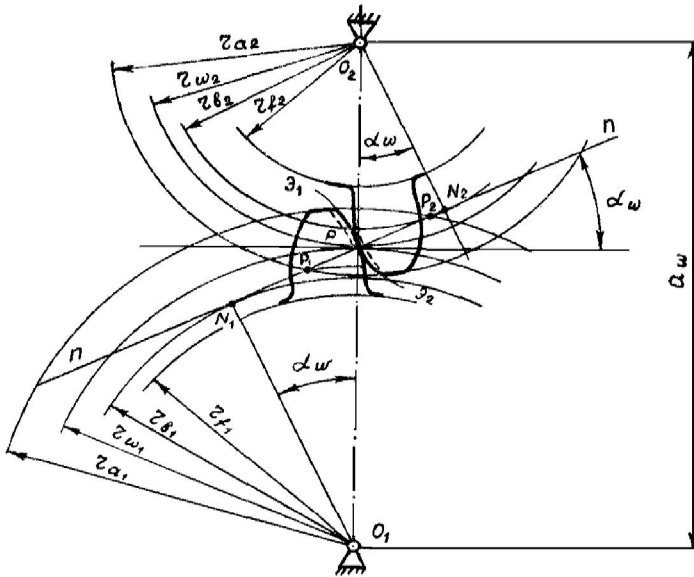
Схема зацепления пары зубчатых колёс.
